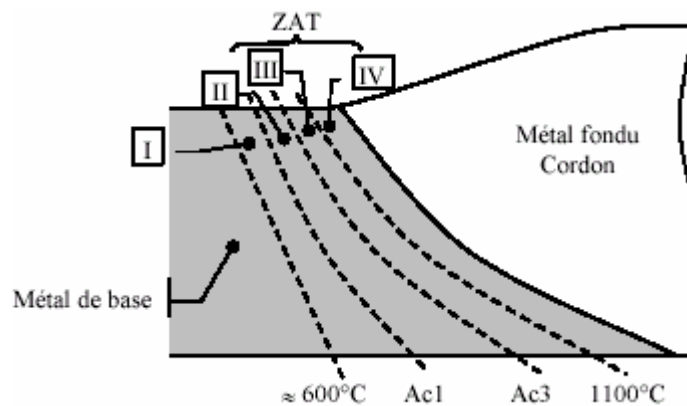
Zone affectée thermiquement d'un cordon de soudure
